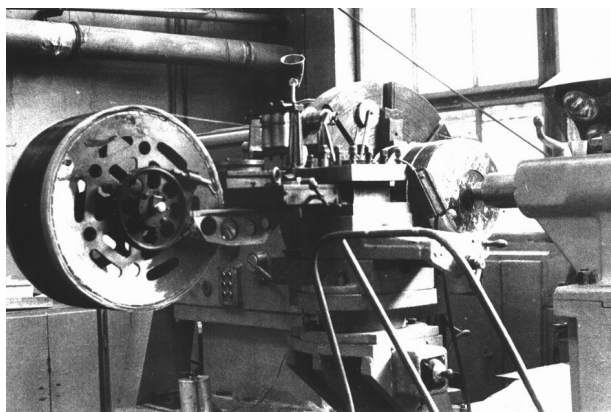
Устройство для намотки трубчатых заготовок на модернизированном токарном станке
